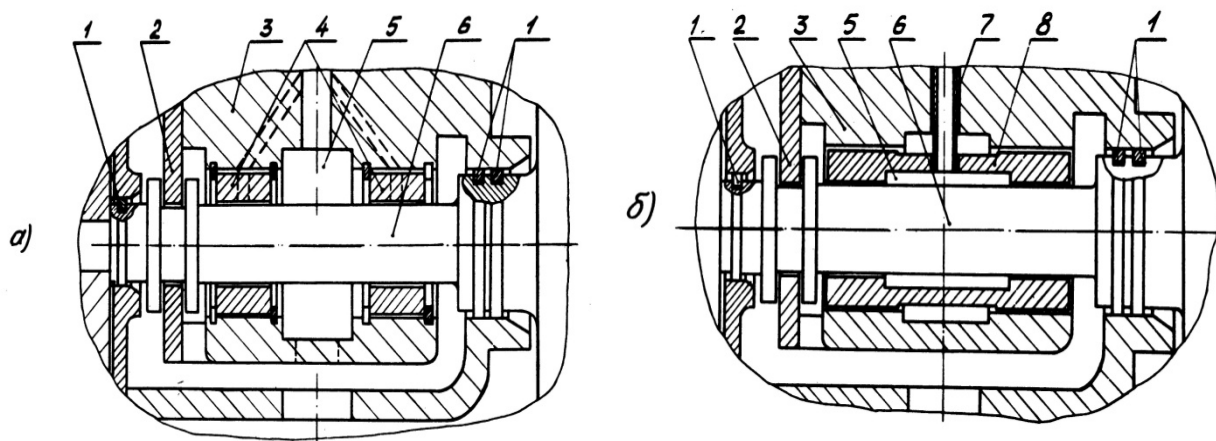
Конструкции узлов подшипников ТКР [1]:
